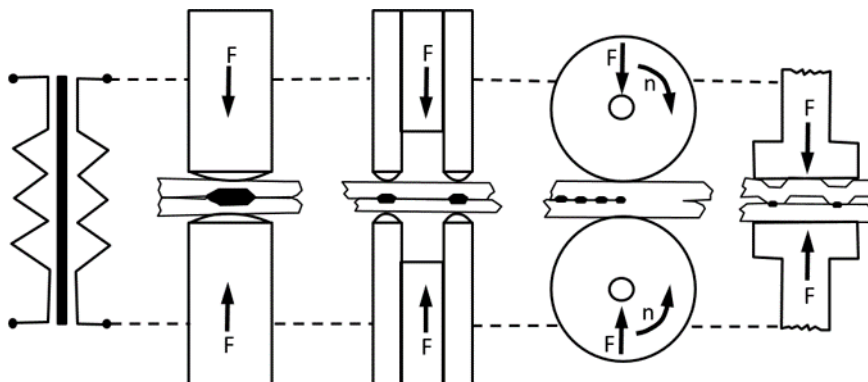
Aperçu des procédés de soudage par résistance [98]
